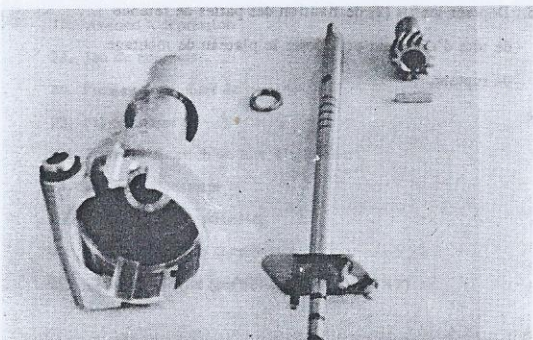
Dépose de l'axe de régulateur centrifuge.
